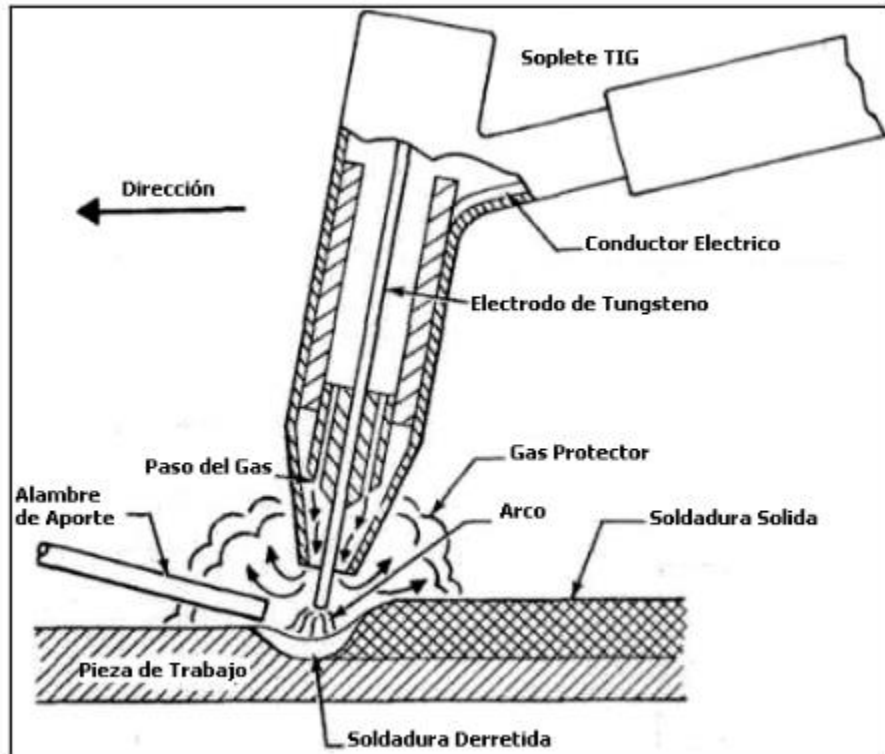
Esquema de un soplete para soldadura TIG [Haynes Techbook Welding Manual] [18]
